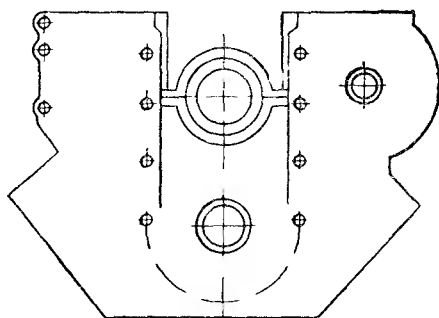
Положение блока цилиндров на конвейере при установке коленчатого вала
